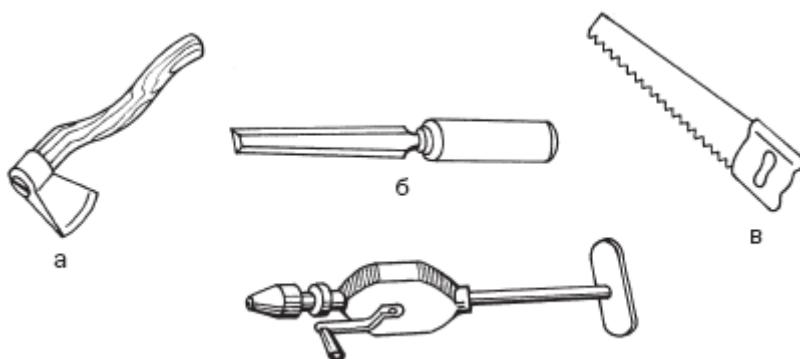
Инструменты плотника: а – топор; б – стамеска; в – ножовка; г – ручная дрель
